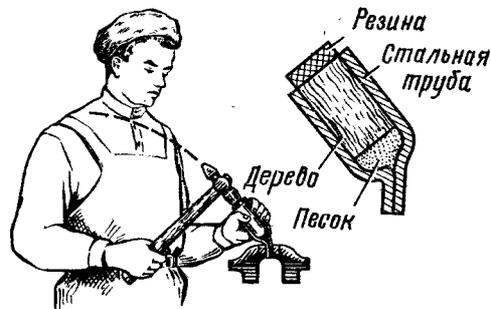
Движение руки при кистевом ударе и приспособление для нанесения ударов
